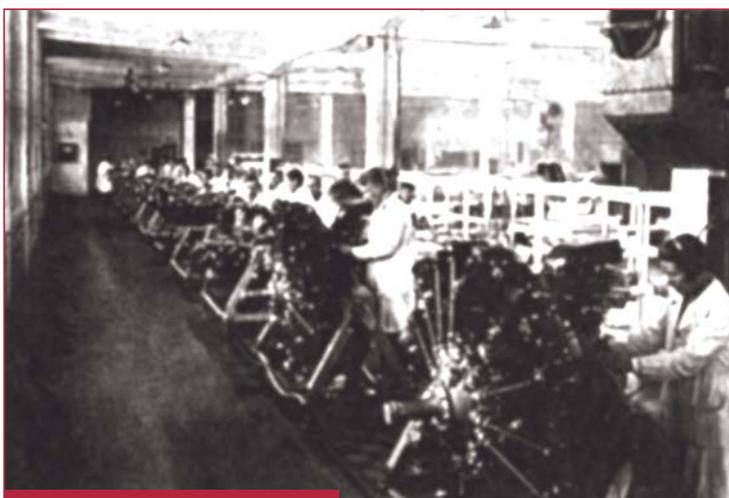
Сборка моторов M-25B : детали кладутся друг на друга, хотя бы
